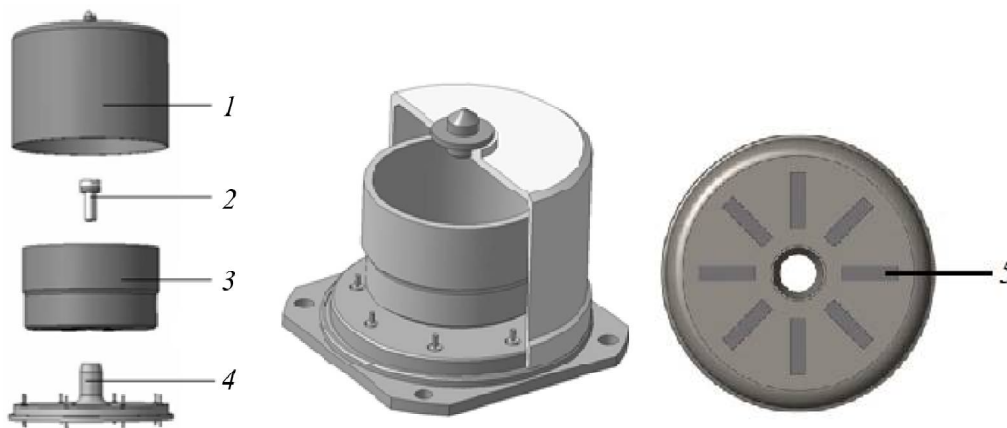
Конструкция ВТГ с металлическим резонатором [3]: 1 – корпус, 2 – крепежный винт, 3 – резонатор, 4 – основание, 5 – пьезоэлементы
